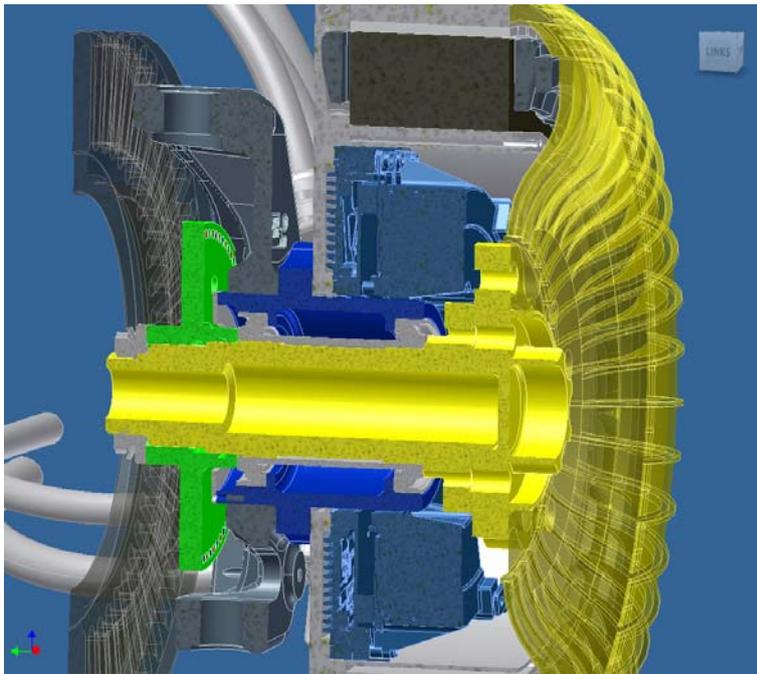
Montageposition der ABS-Sensorik (grün) im Radnabenmotor Package
